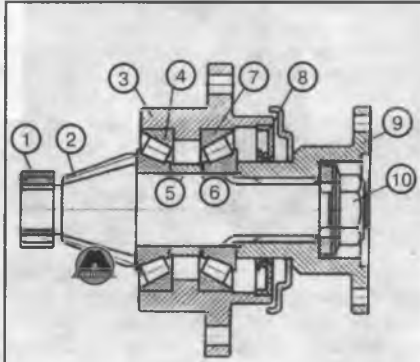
Корпус подшипников с ведущей шестерней в сборе:
